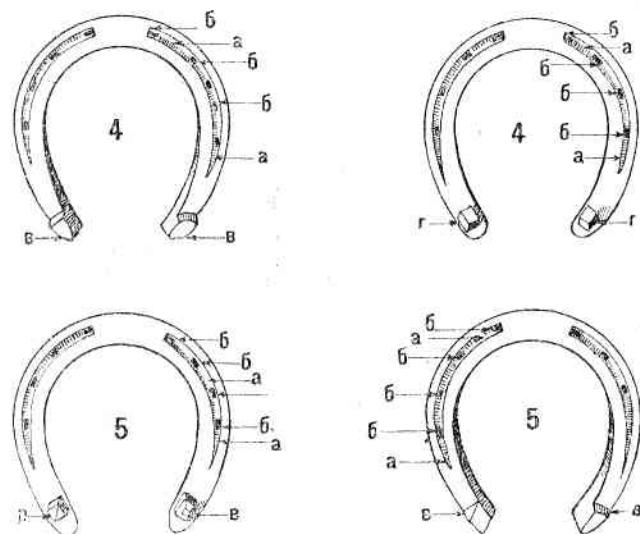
а. Образцы подков. 4 — подкова для верховых лошадей с тупыми шипами зимняя, легкая, не тяжелей 500 г, без захвата, чтобы лошадь не спотыкалась, к концу ветвей утончающаяся; а) дорожка, б) гвоздевые отверстия, в) постоянные шипы, г) винтовые шипы; 5 — подкова для верховых лошадей зимняя с винтовыми шипами (левая) и с постоянными шипами (правая) при остром наружном шипе.
